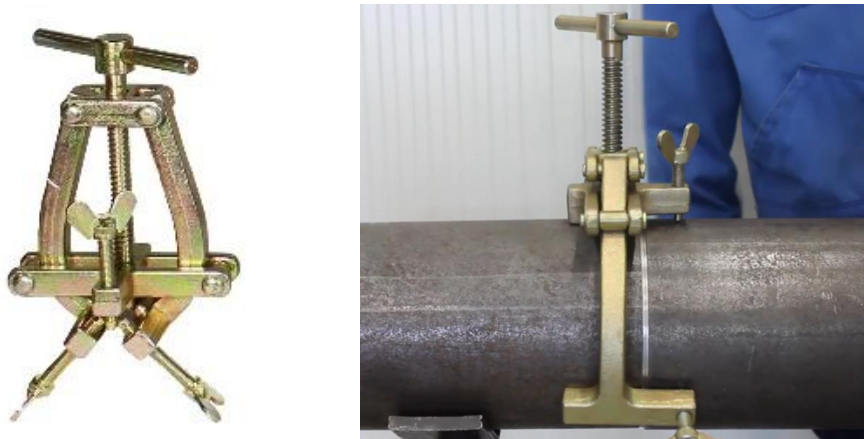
Alineamiento de cupón de soldadura
